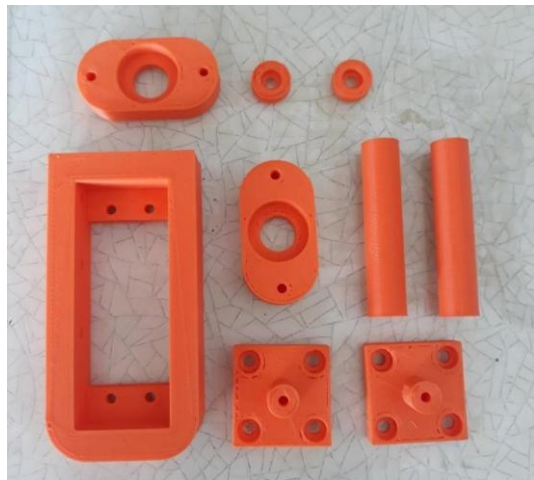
Надруковані деталі рукоятки робота-маніпулятора
